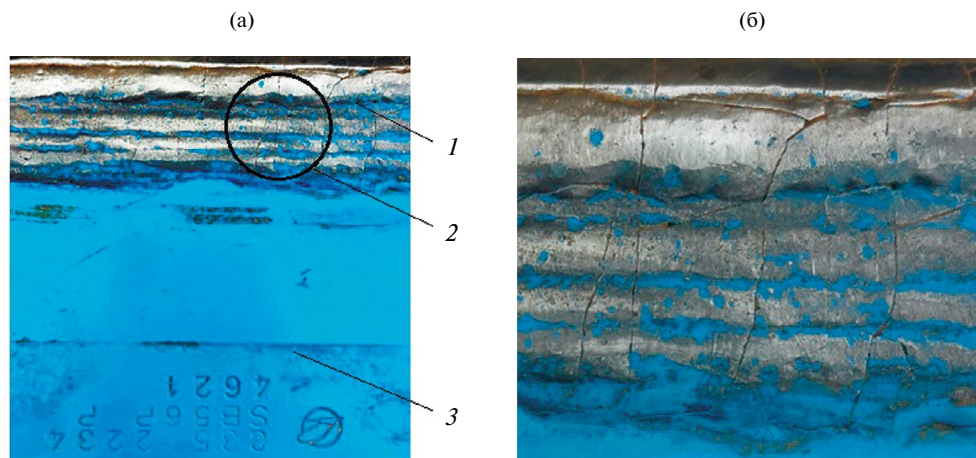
Фрагменты ножа: (а) — тыльная сторона с абразивостойкой наплавкой; (б) — трещины в наплавленном металле; 1 — наплавленный слой; 2 — трещины; 3 — металл ножа.
